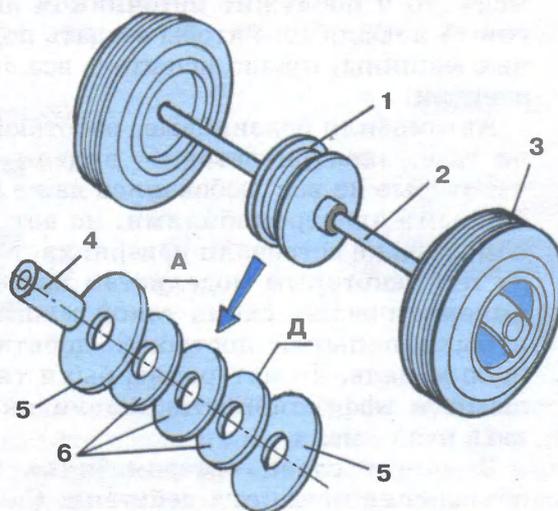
Ведущий мост модели: 1 — шкив; 2 — ось; 3 — колесо; А — детали шкива; 4 — втулка; 5 — боковые шайбы; 6 — внутренние шайбы (Д — равен передаточному отношению).
